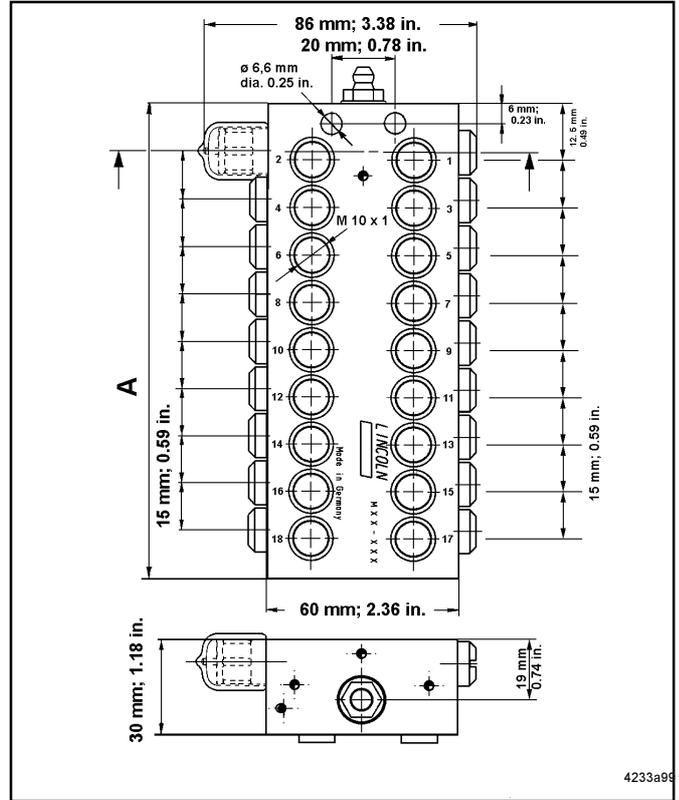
Cotes dimensionnelles du doseur SSV installé à l'arrière
